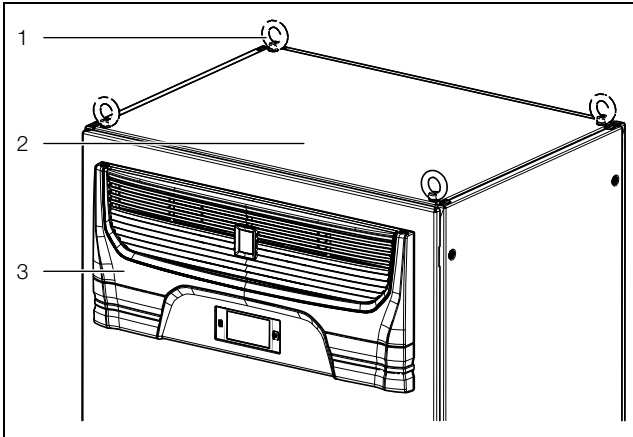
Рым-болты для транспортировки в верхней части шкафа
